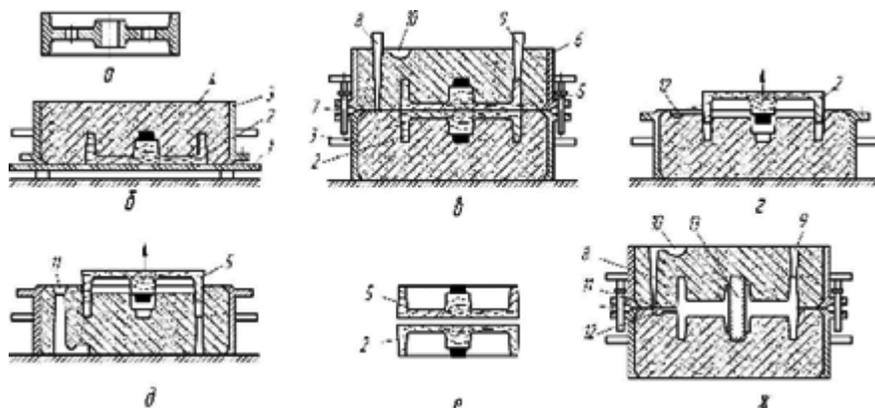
Форма для изготовления шкива, выполненная в двух опоках: а - деталь; б, в, г, д - операции изготовления формы; е - модель; ж - собранная форма
